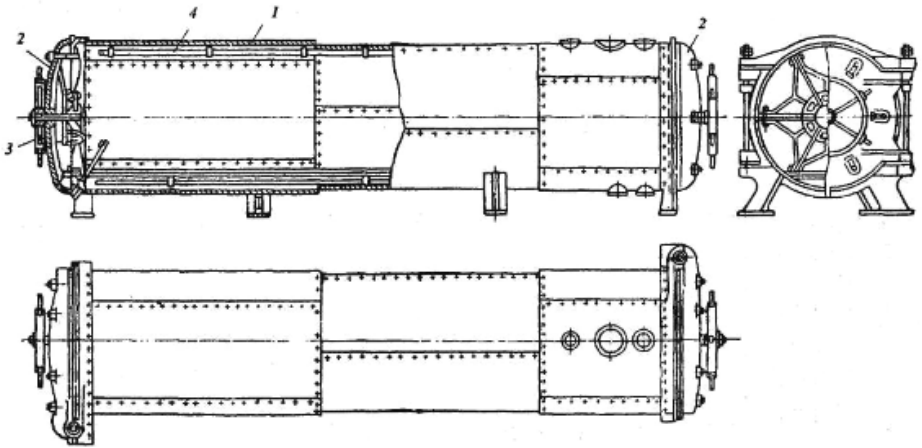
Горизонтальний автоклав: 1 – корпус; 2 – кришка; 3 – затискний пристрій; 4 – барботер.
